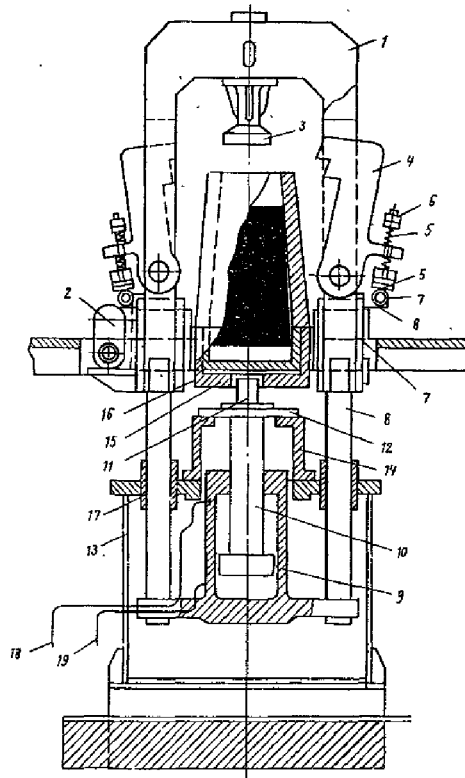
Пристрій для виштовхування злитка з виливниці
